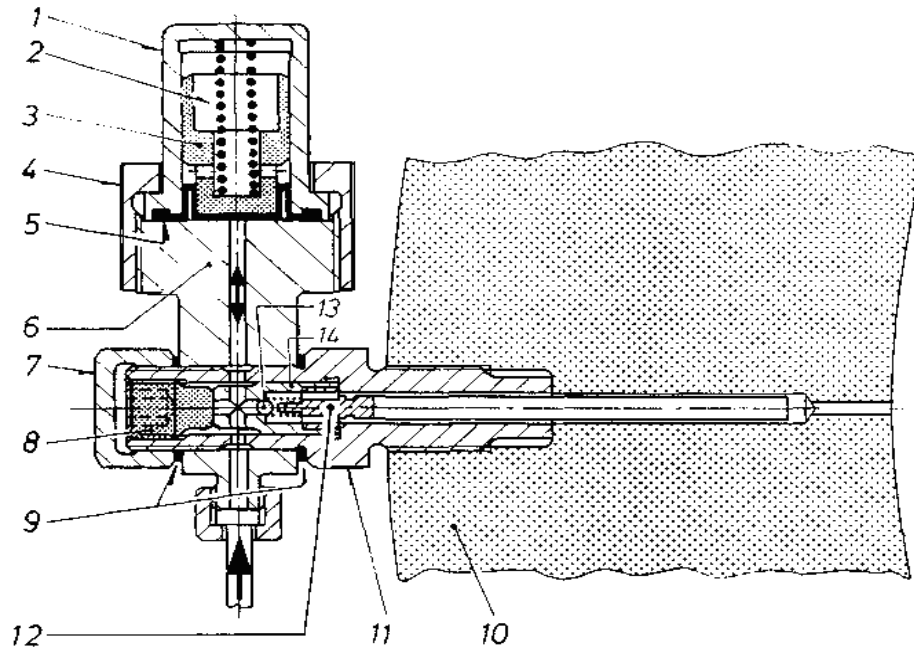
Конструкция маслоподводящего устройства двигателя RTA Sulzer: 1 — крышка аккумулятора; 2 — пружина; 3 — поршень; 4 — накидная гайка; 5 — мембрана; 6 — корпус аккумулятора; 7 — гайка штуцера; 8 — болт; 9 — шайбы; 10 — цилиндрическая втулка; 11 — штуцер; 12 — стержень; 13 — клапан; 14 — корпус клапана
